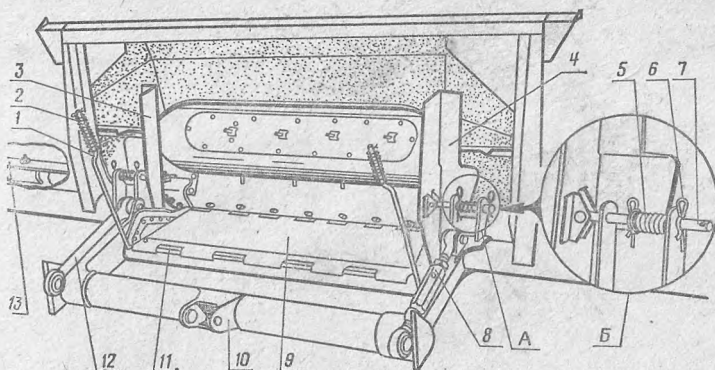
Установка щитков уплотнений и отражателей жатки:
